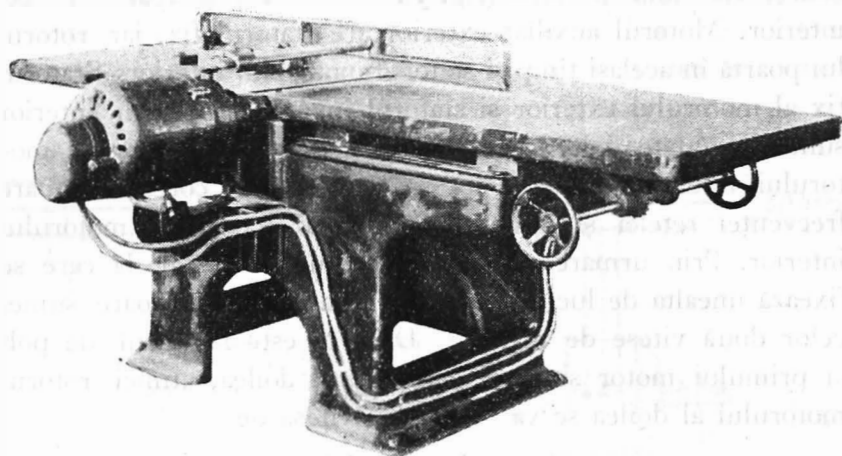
Mașină de rânduit (Abrichtmaschine) cu motor dublu.
